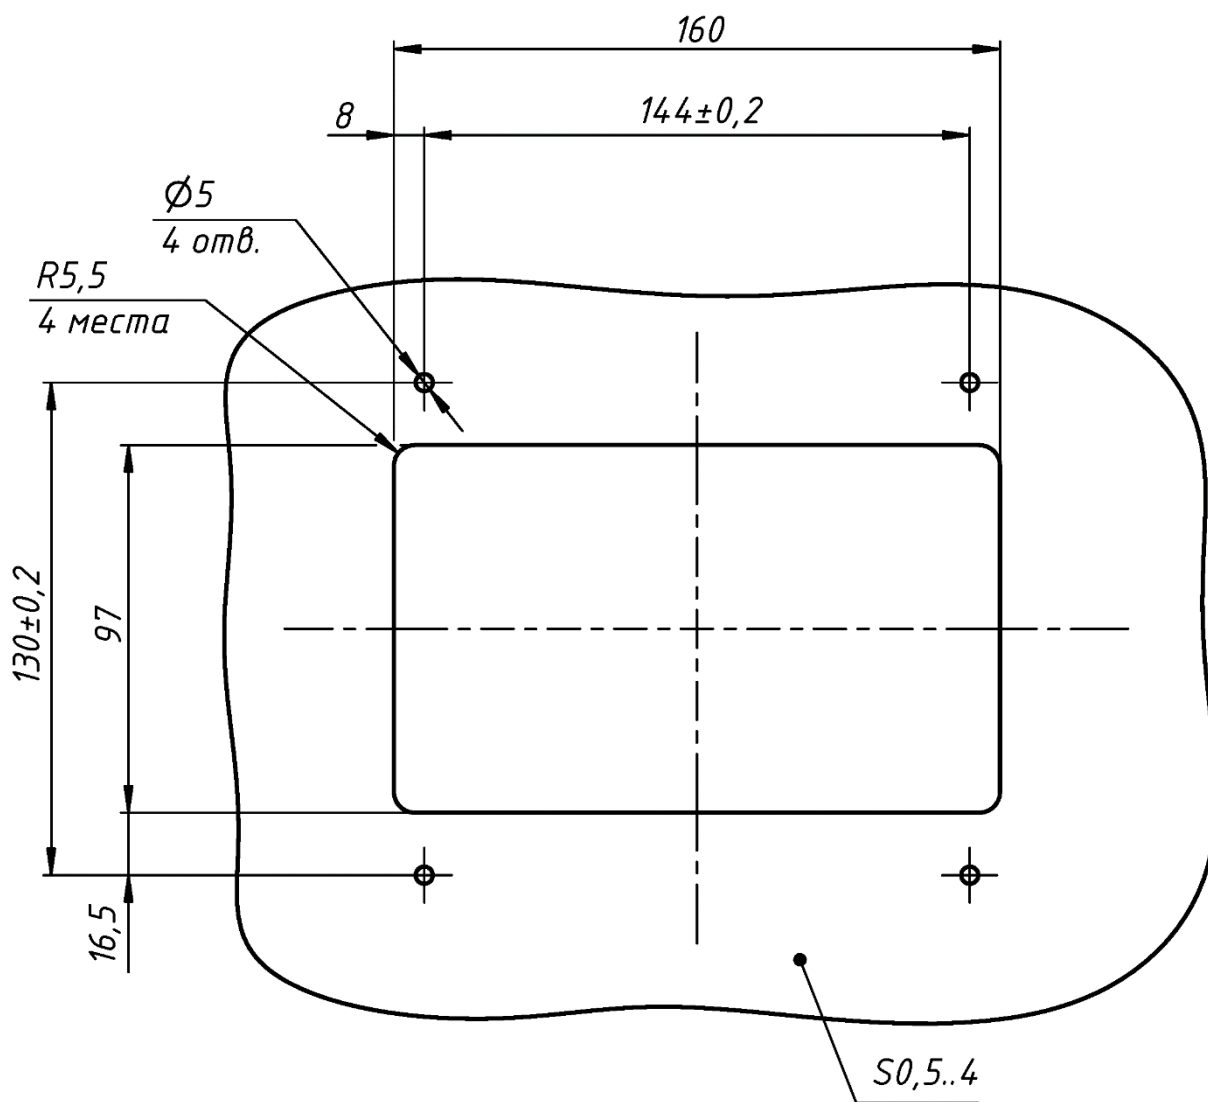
Чертеж места установки ПРОЭЛ-МИНИ-01
